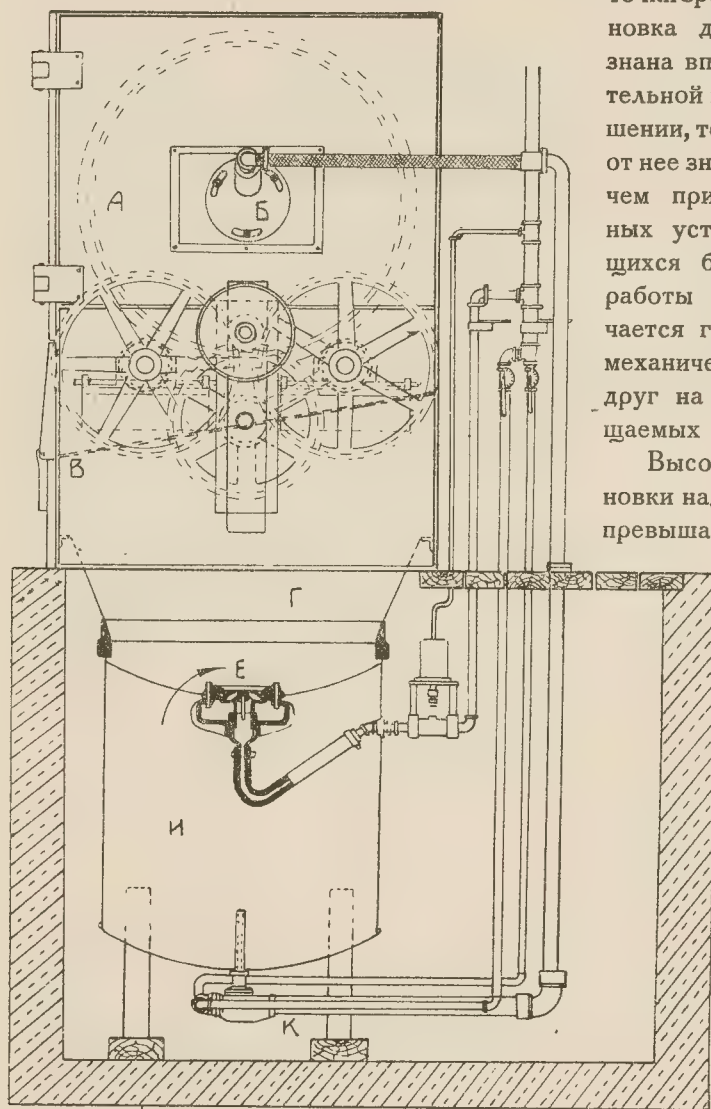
Схема барабанной очистки отливок под давлением струи песка.
